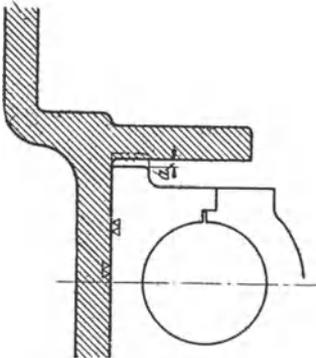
Zu enger Zwischenraum bei Gußstücken ohne Bearbeitung.
